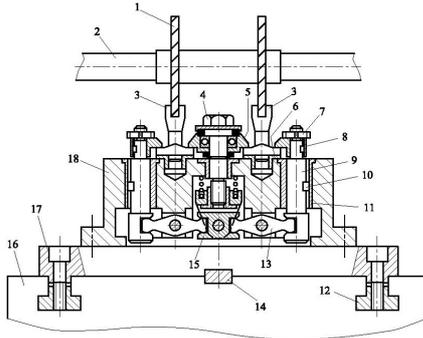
Doppelspannvorrichtung zum Fräsen von zwei Werkstücken
